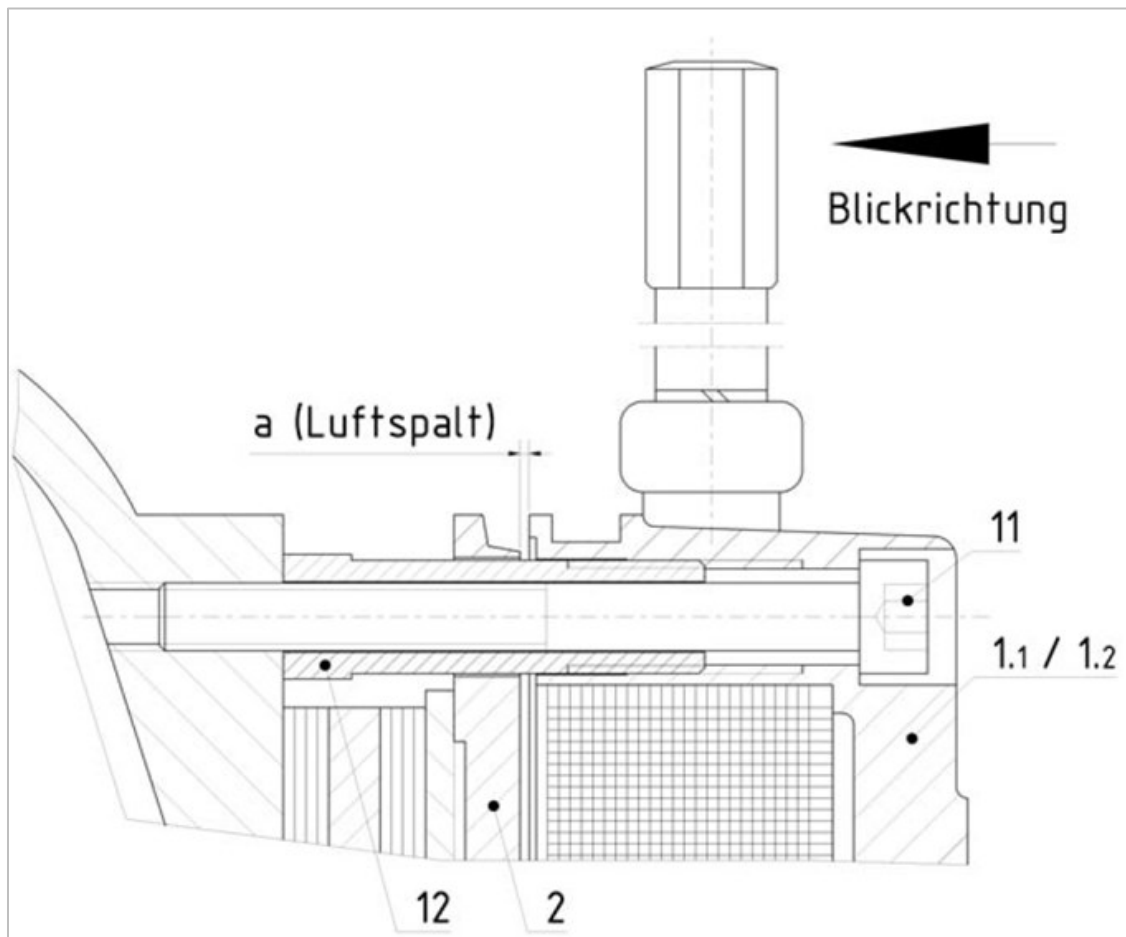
Réglage du jeu de freinage type FDB / FDD
